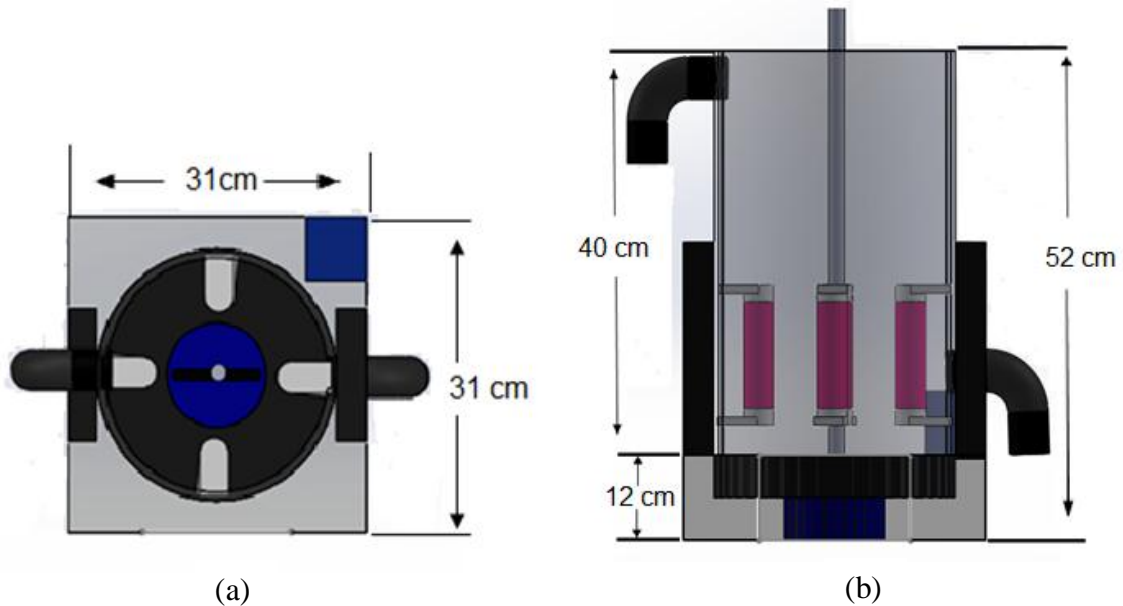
dimensiones del fotorreactor, vistas frontal (b) y vista inferior (a)
